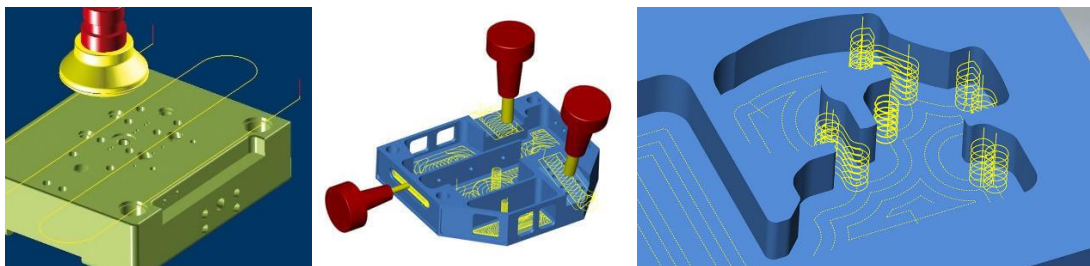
Soustružnicko-frézovací modul millTURN [40]
